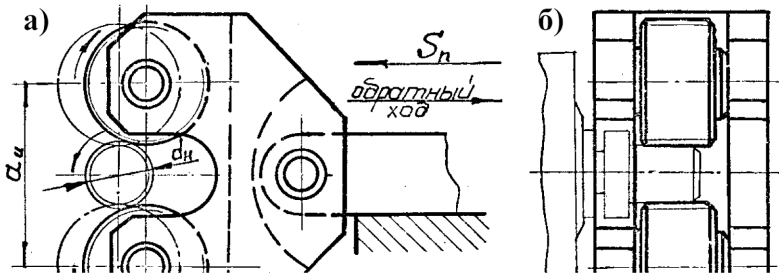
Схема накатывания цилиндрической резьбы: главный вид (а), вид сбоку (б)
